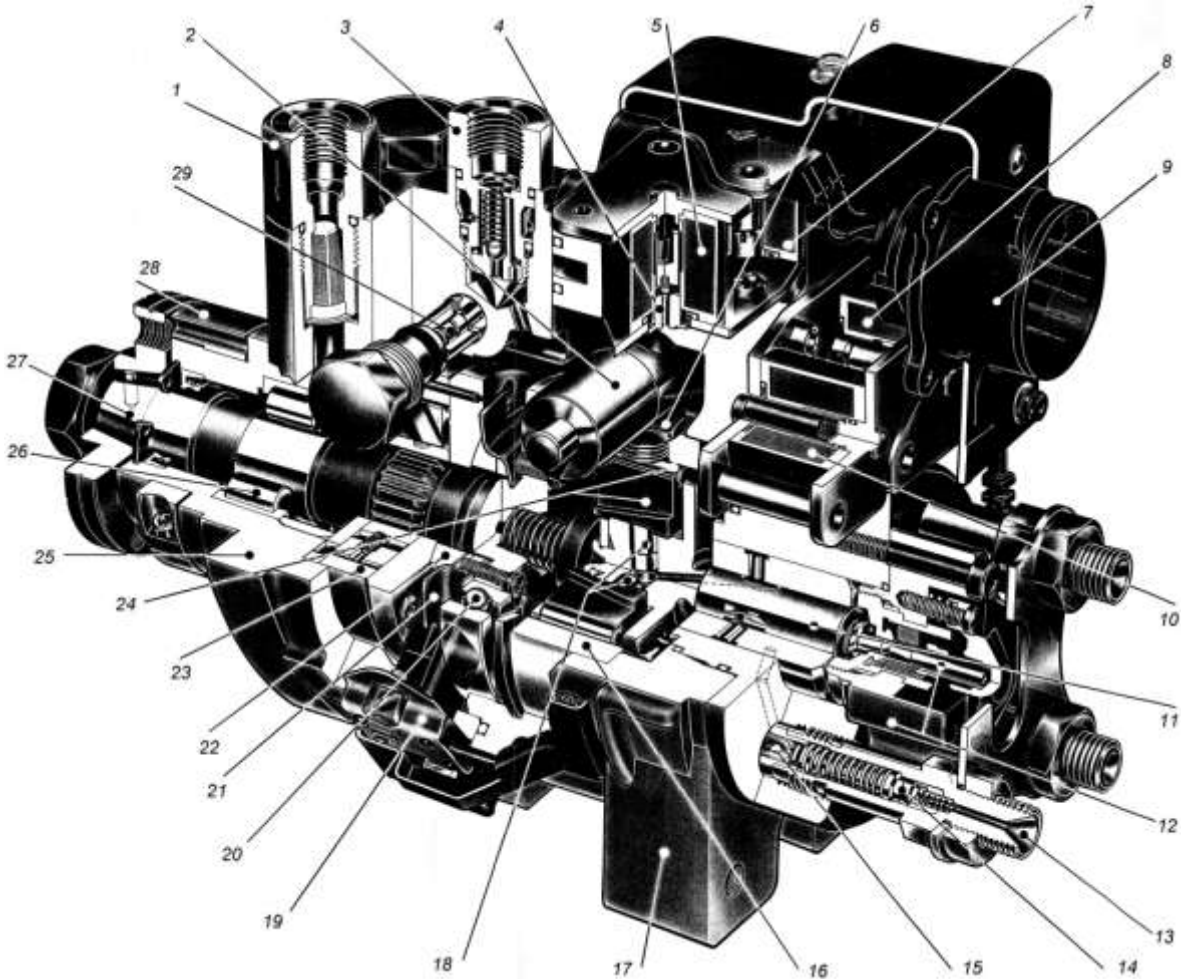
Общий вид ТНВД EPIC-80: 1 - штуцер подвода топлива; 2 - сервопоршень регулирования УОВТ; 3 - штуцер слива; 4 - седло шарикового клапана; 5 - актюатор УОВТ; 6 - болт-поводок кулачковой шайбы; 7 - актюатор дренажа управления ротором; 8 - актюатор подачи управления ротором; 9 - разъем; 10 - электромагнит прерывания ТП; 11 - ротор; 12 - датчик осевого положения ротора; 13 - нагнетательный штуцер; 14 - демпфирующий клапан; 15 - нагнетательный клапан; 16 - кулачковая шайба; 17 - средняя опора; 18 - плунжеры; 19 - датчик углового положения вала; 20 - внешний шариковый подшипник; 21 - кольцо измерения частоты вала; 22 - внутреннее кольцо сферической опоры; 23 - роторно-лопастной ТПН; 24 - ролик кулачковой шайбы с толкателем; 25 - корпус привода; 26 - передний подшипник; 27 - приводной вал; 28 - адаптер регулировки УОВТ; 29 - регулятор давления подкачки.
